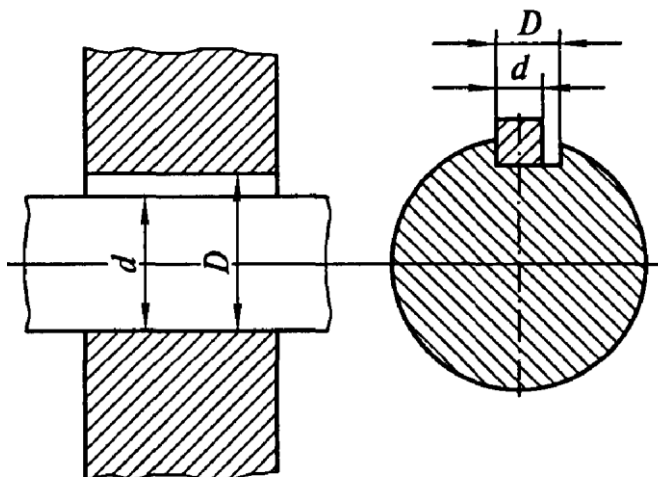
Примеры охватываемой и охватывающей поверхностей
